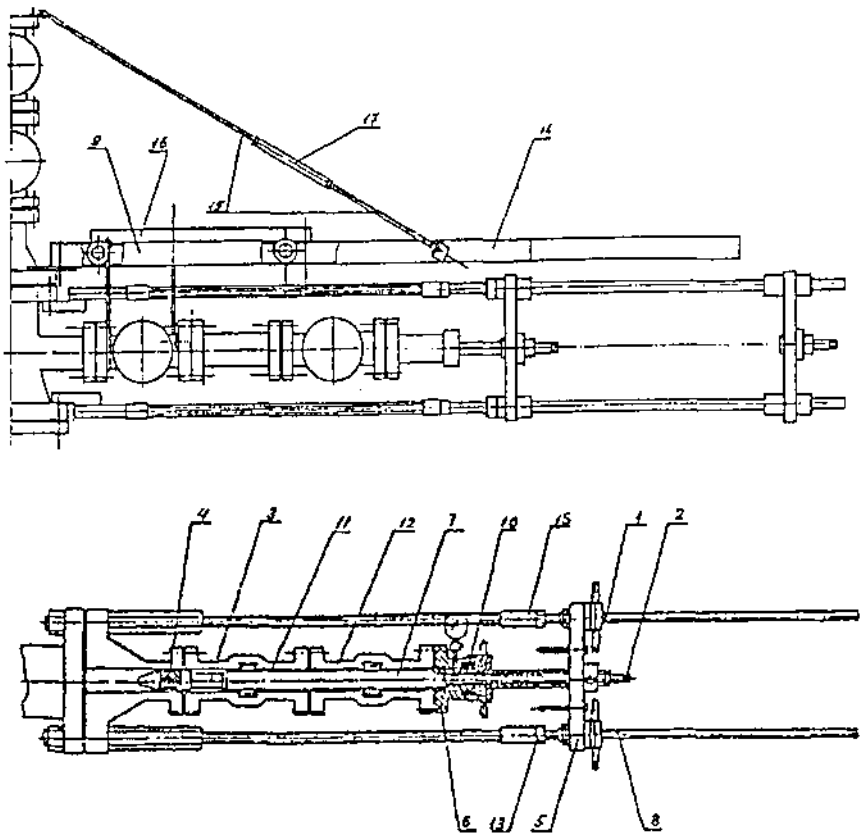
Устройство для смены задвижек фонтанной арматуры под давлением
